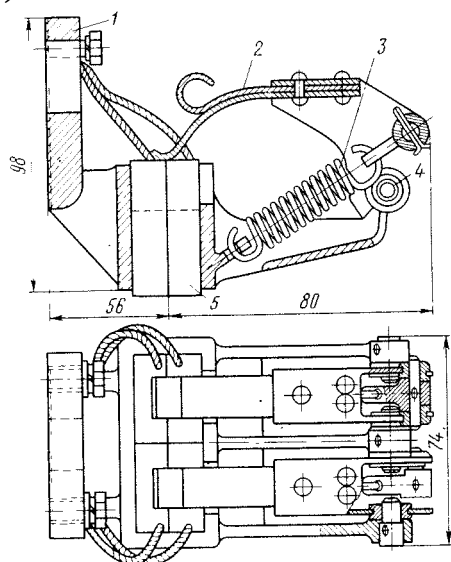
Щеткодержатель тягового двигателя РТ-51М
